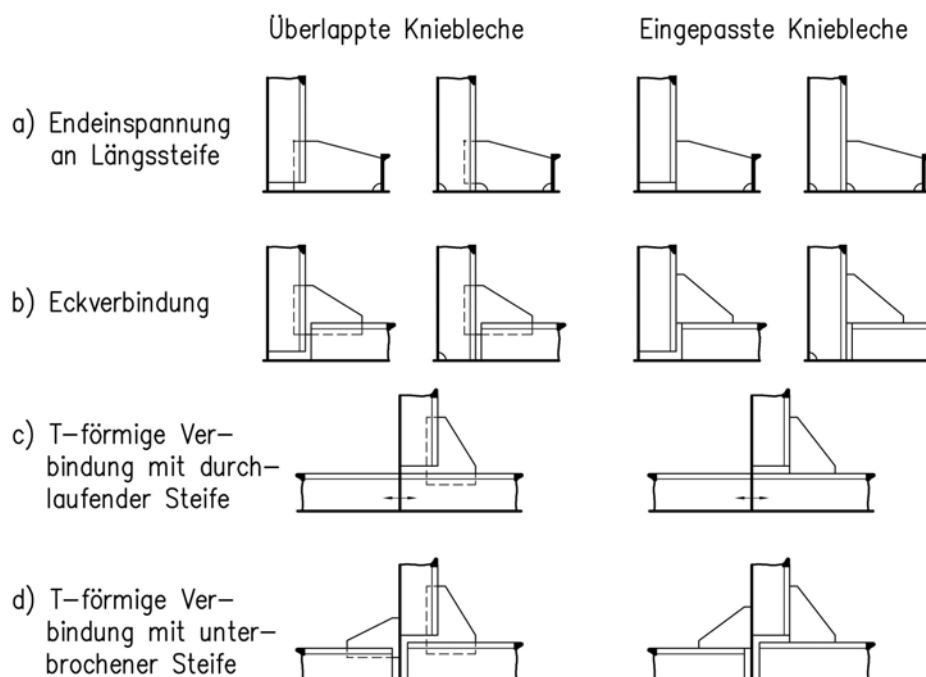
Überlappte und eingepasste Knieblechanschlüsse
